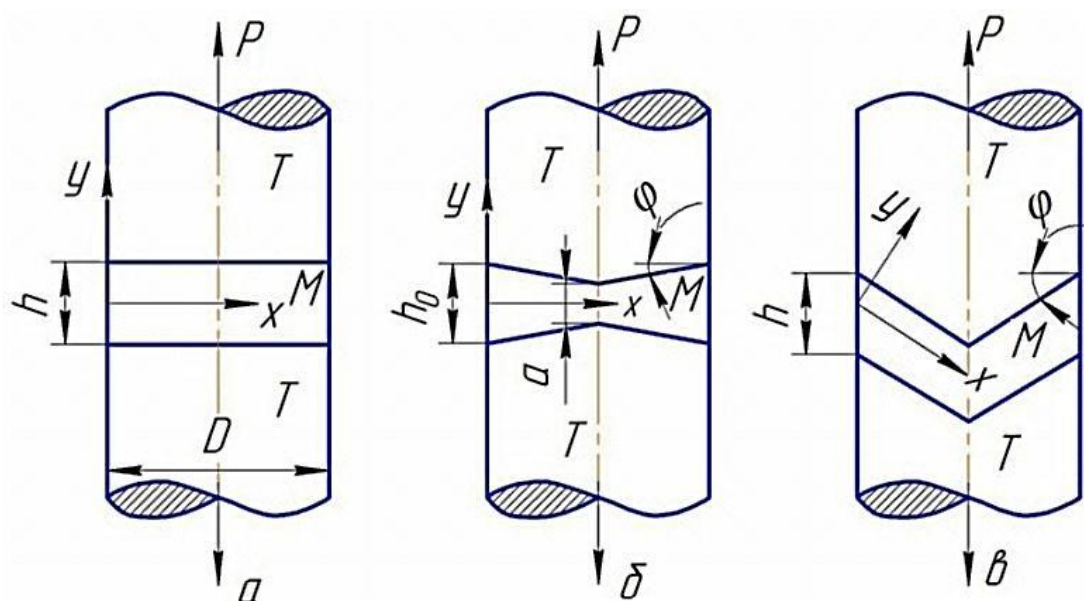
Типові схеми осьового розтягування циліндричних стикових зварних з'єднань із різною геометрією прошарку: а – прямокутний; б – Х-подібний; в – шевронний варіант з'єднання..
